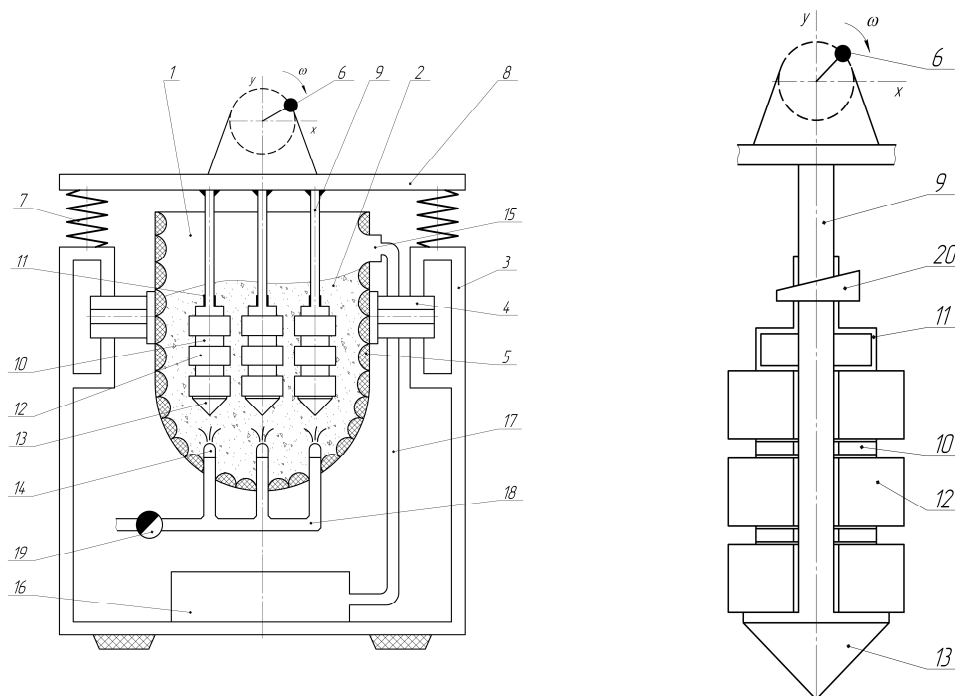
Принципиальная схема вибростанка модели ВГ-250 и схема базирования и закрепления обрабатываемых деталей на установочных пальцах колебательной системы
